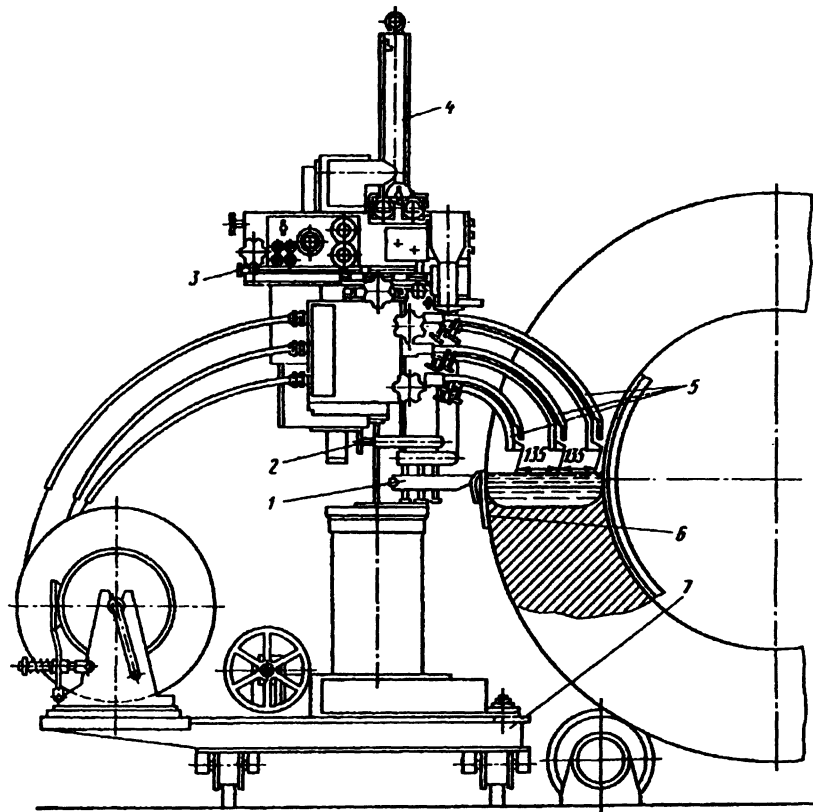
Установка для электрошлаковой сварки кольцевых швов с автоматом А535:
